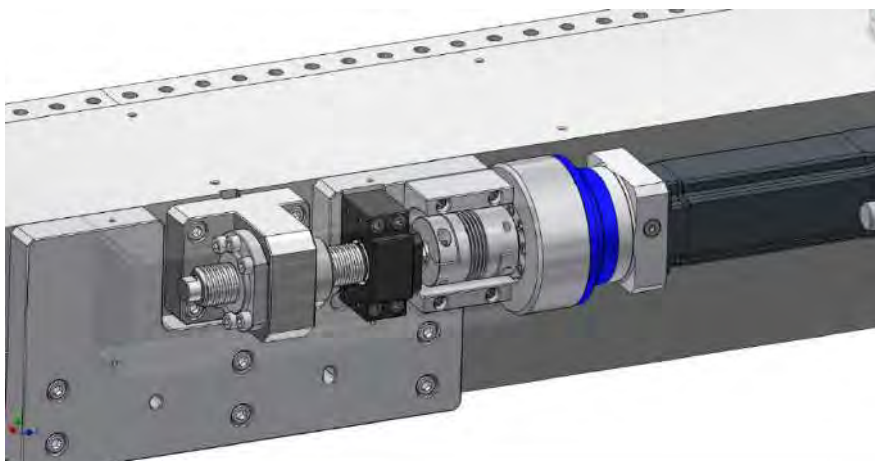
Conjunto mecânico do sistema de movimentação do cassetete.
